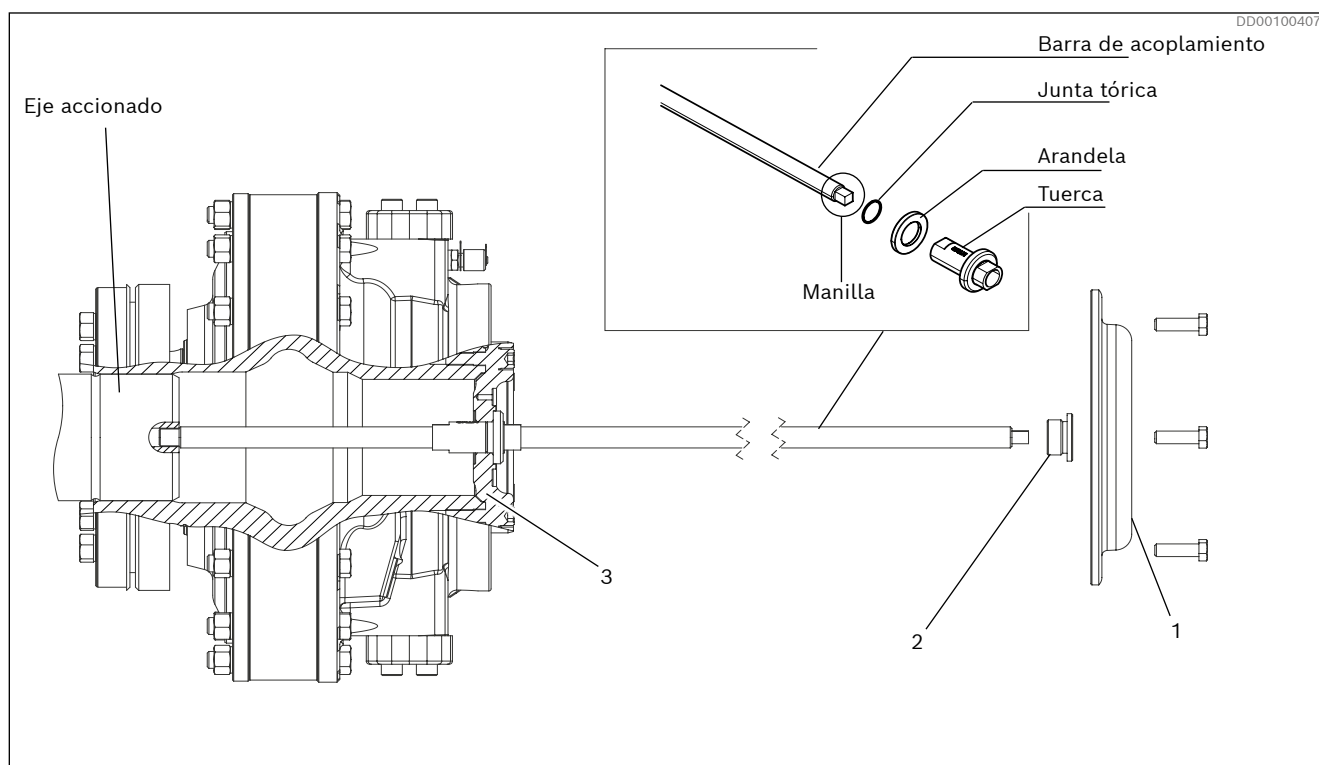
Instalación del motor de acoplamiento con la herramienta de montaje
